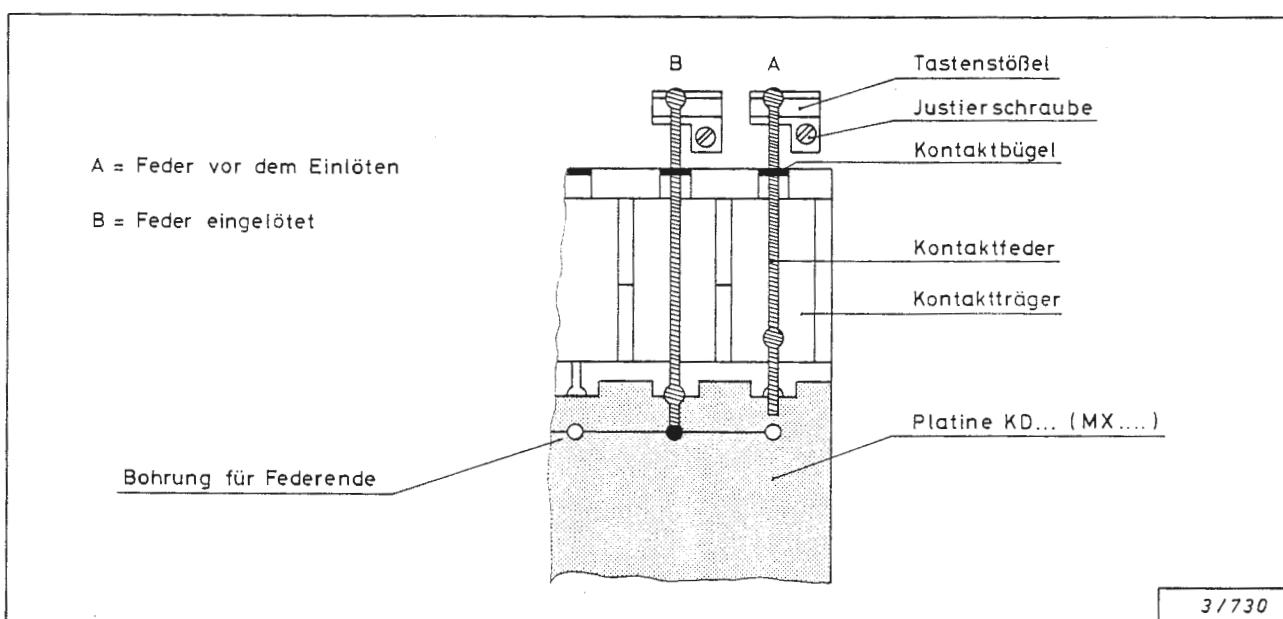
Einspannen der Kontaktfedern (Draufsicht)
